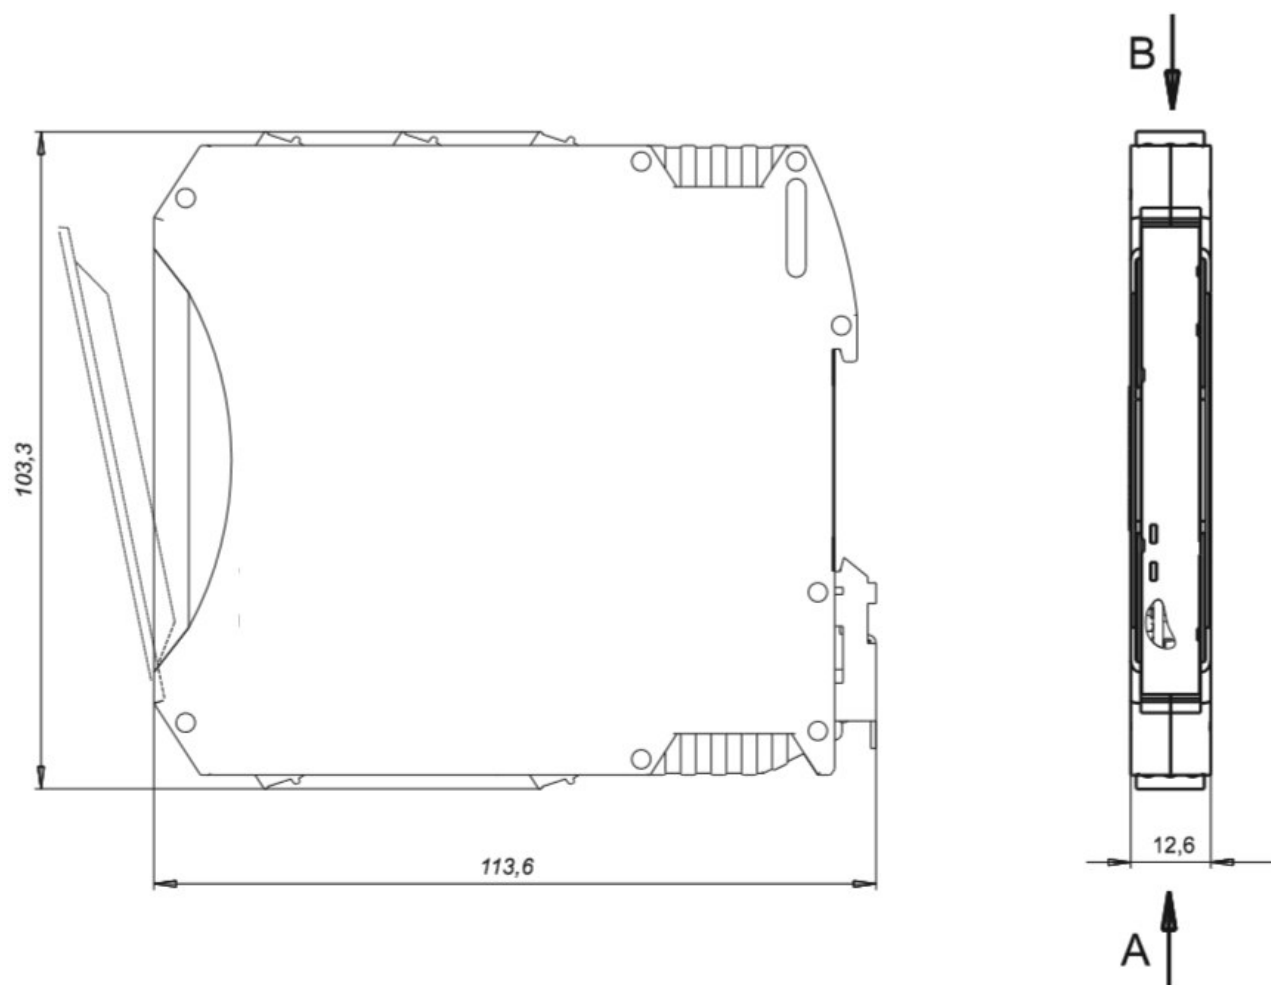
Внешний вид и габаритный чертеж барьера искрозащиты ET A 152
